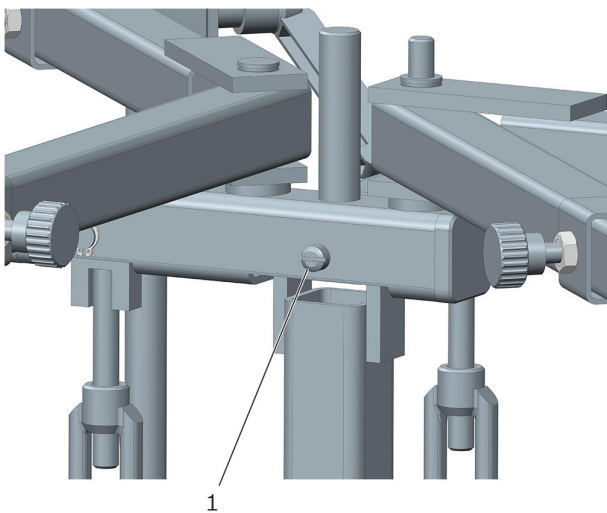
Position Schaftschraube 1, Schaftschraube 2 gegenüberliegend (verdeckt)
